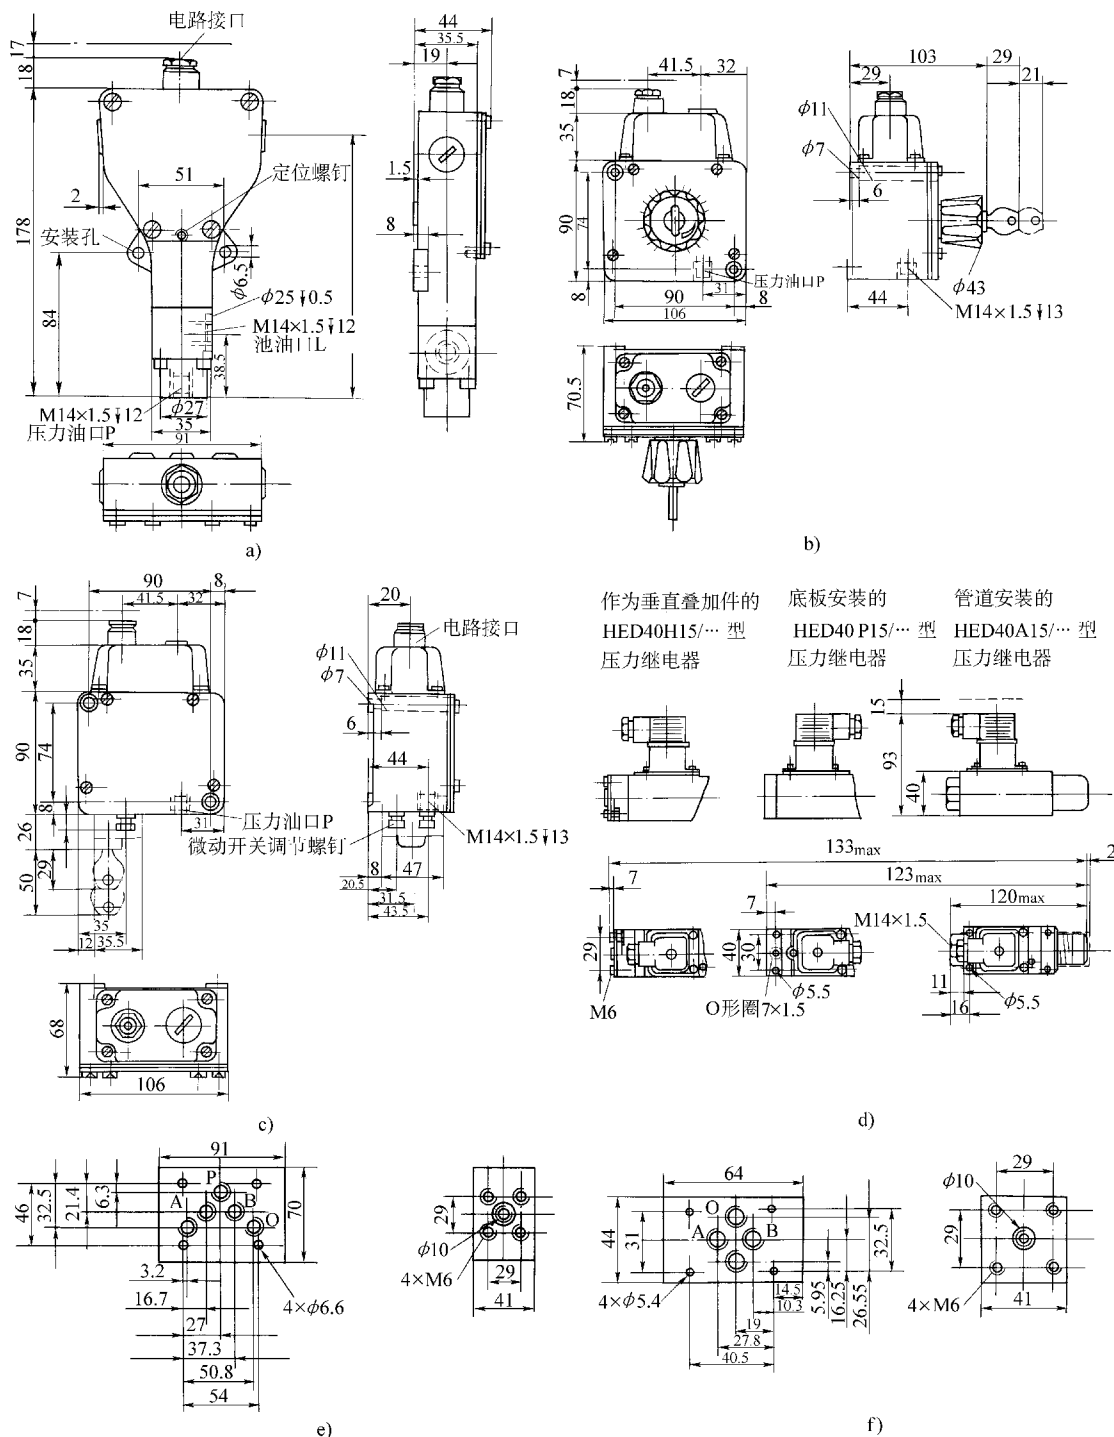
HED 型压力继电器外形尺寸及叠加板尺寸
